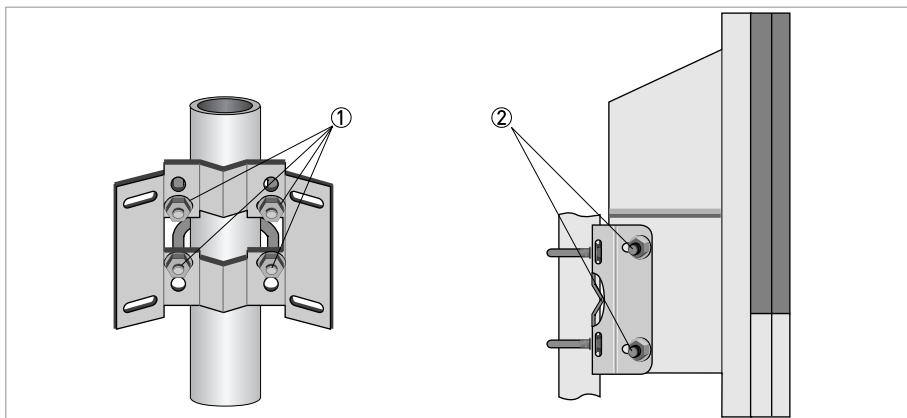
Крепление корпуса преобразователя сигналов для настенного монтажа на стойке
